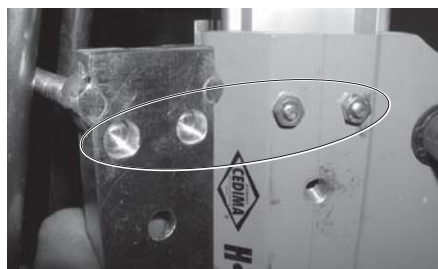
Пластина крепления гидроцилиндра с пазами под болты салазок Н•201
